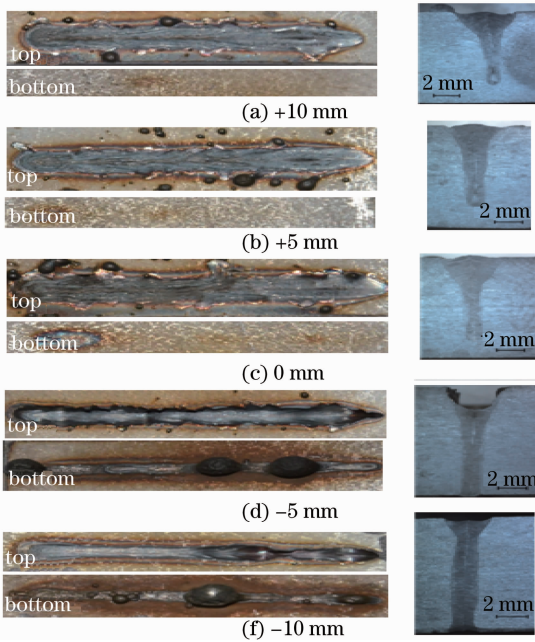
不同离焦量时焊缝表面形貌和截面
